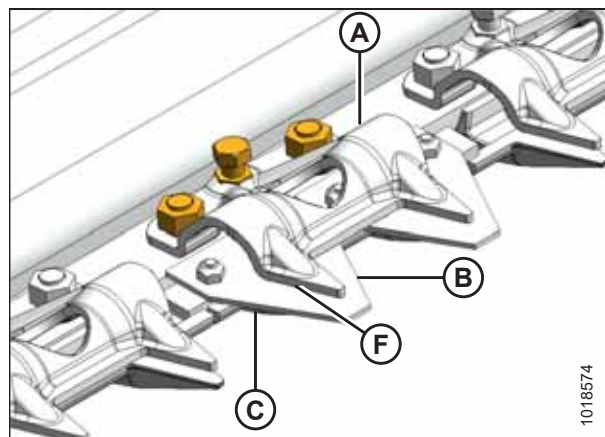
Стандартный прижим из листового металла для тупого противорежущего пальца
